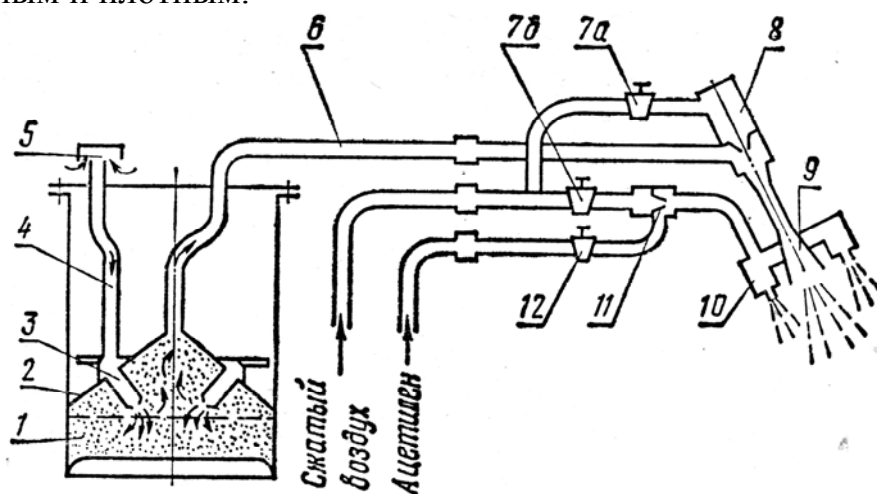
Схема работы установки для газопламенного напыления пластмасс: 1 – порошок; 2 – колпак; 3 – сопло; 4 – резиновая трубка; 5 – гайка-фильтр; 6 – трубка для подачи порошково-воздушной смеси; 7а, 7б и 12 – вентили; 8 – порошковый инжектор; 9 – порошковое сопло; 10 – кольцевое сопло газовой горелки; 11 – смесительная камера
